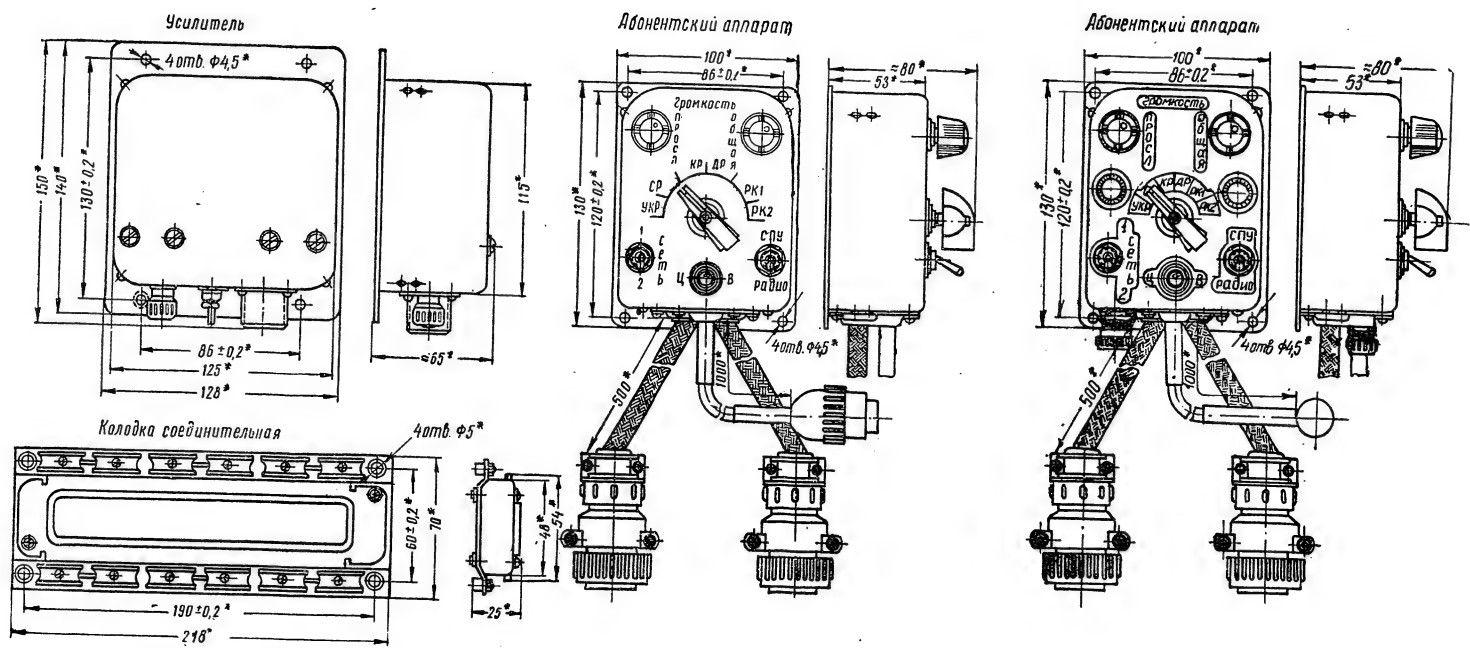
Габаритно-установочные размеры блоков изделия СПУ-7
